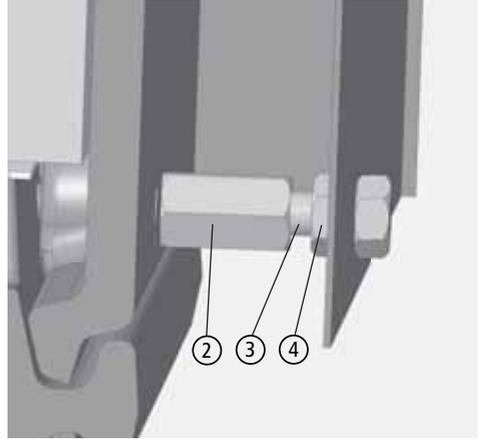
untere Befestigungspunkte, Verschraubungen
